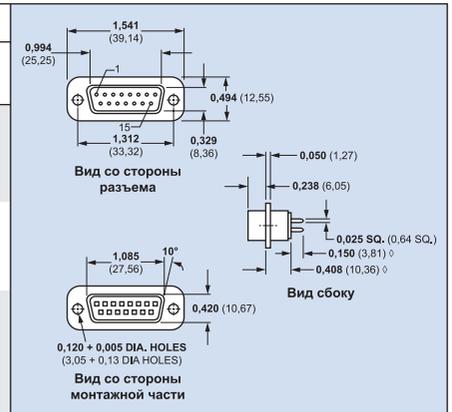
Пример номера для заказа фильтрующего разъема D-SUB и его габаритные размеры
